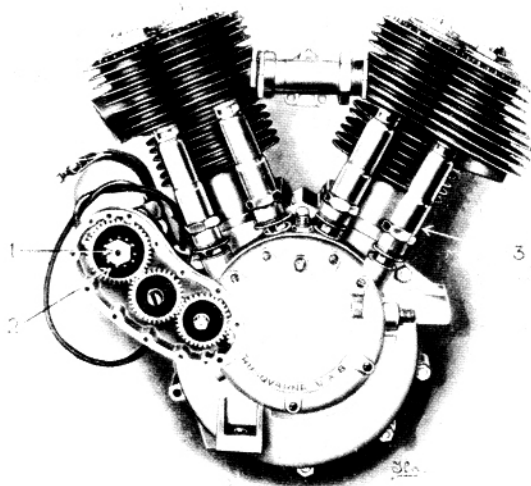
Motor mod. 610 med locket till magnetdrivningshuset borttaget.
